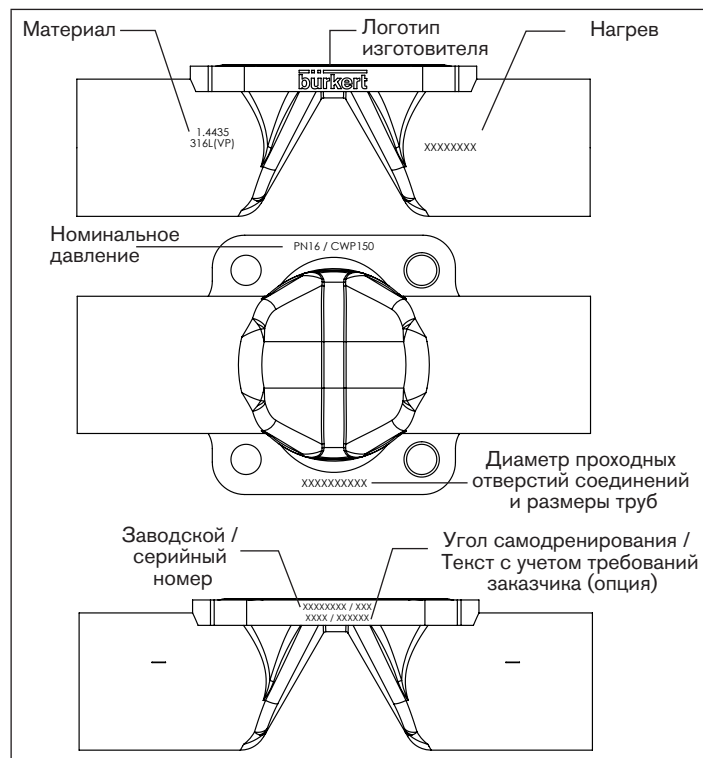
Маркировка трубчатого корпуса клапана (VP)
